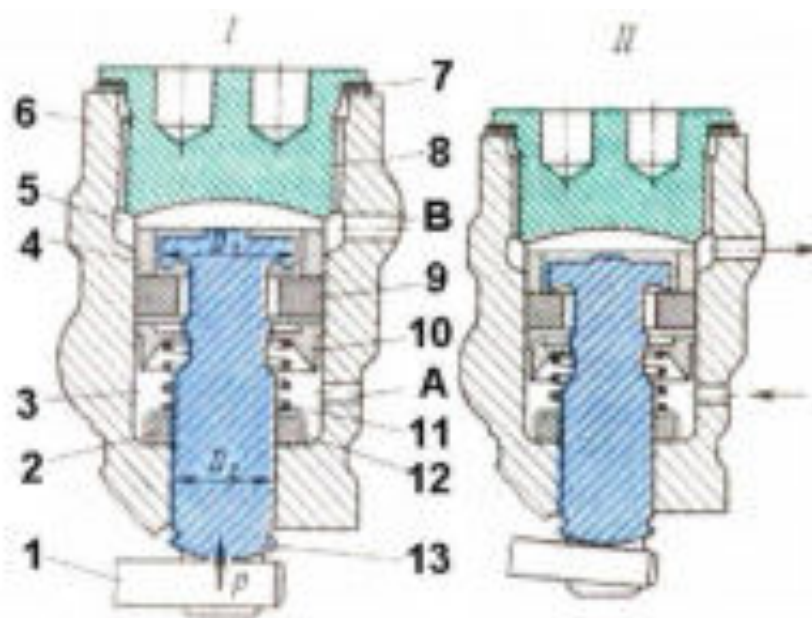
Устройство колесного тормозного цилиндра.
